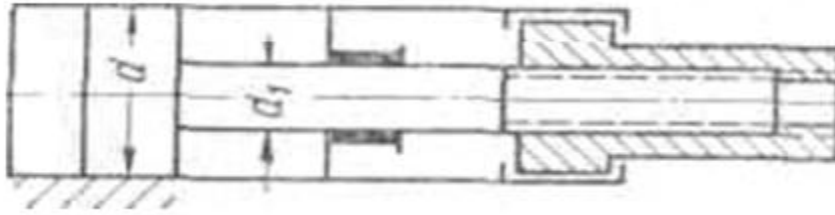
Схема гидроцилиндра с винтовой передачей
